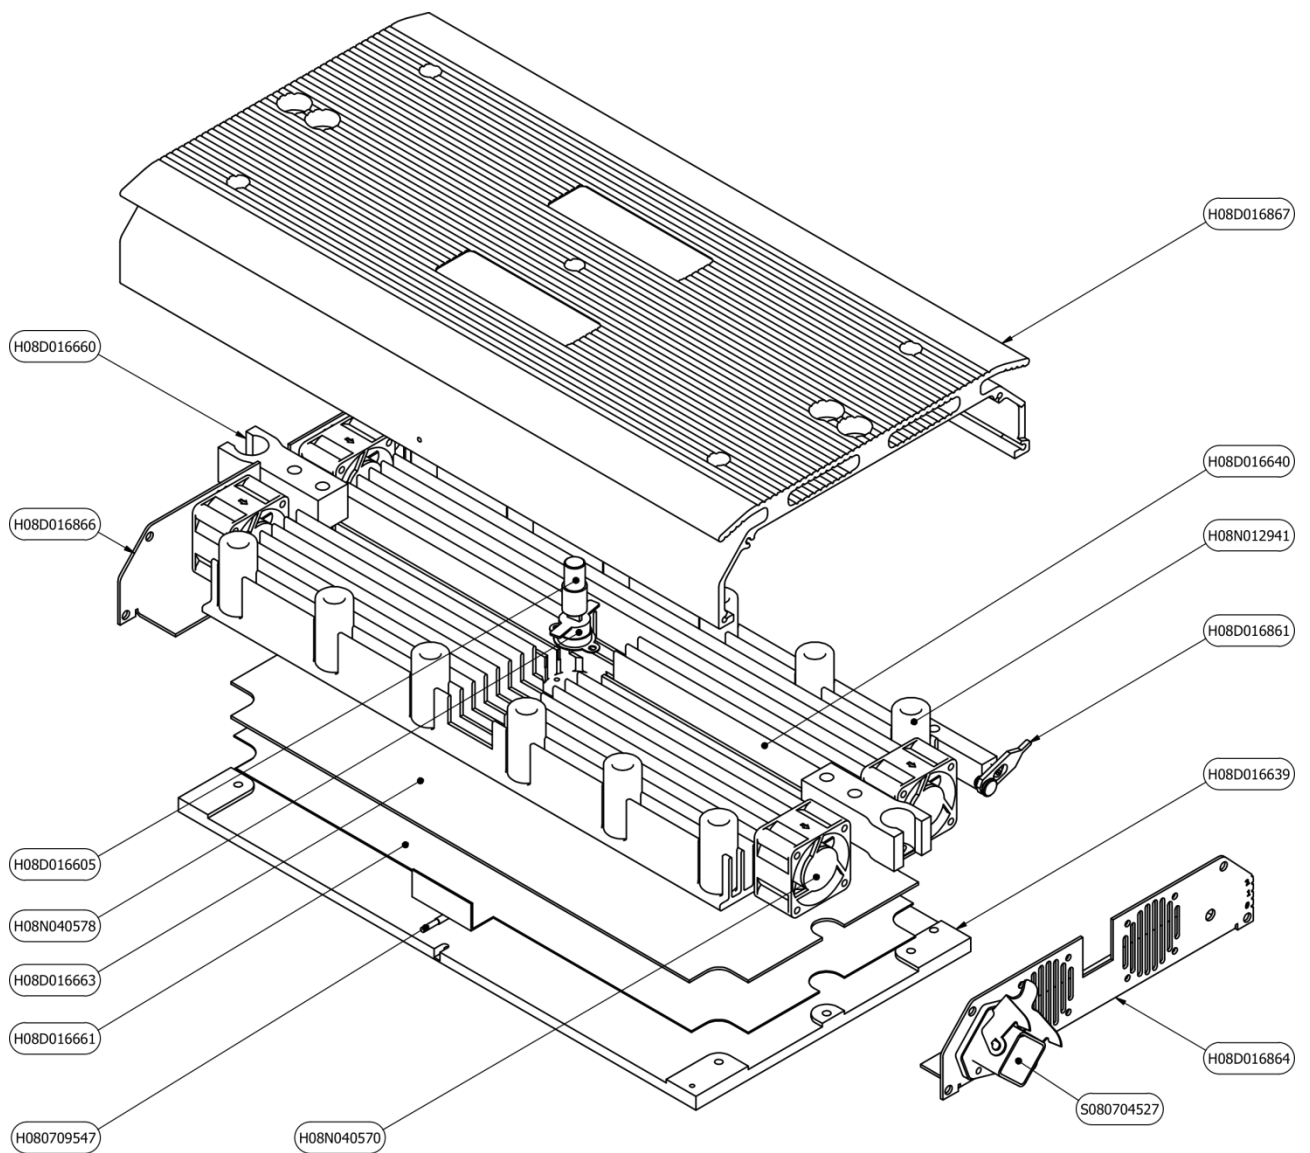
H08D016638 Assemblage de plaque chauffante supérieure PML-300
